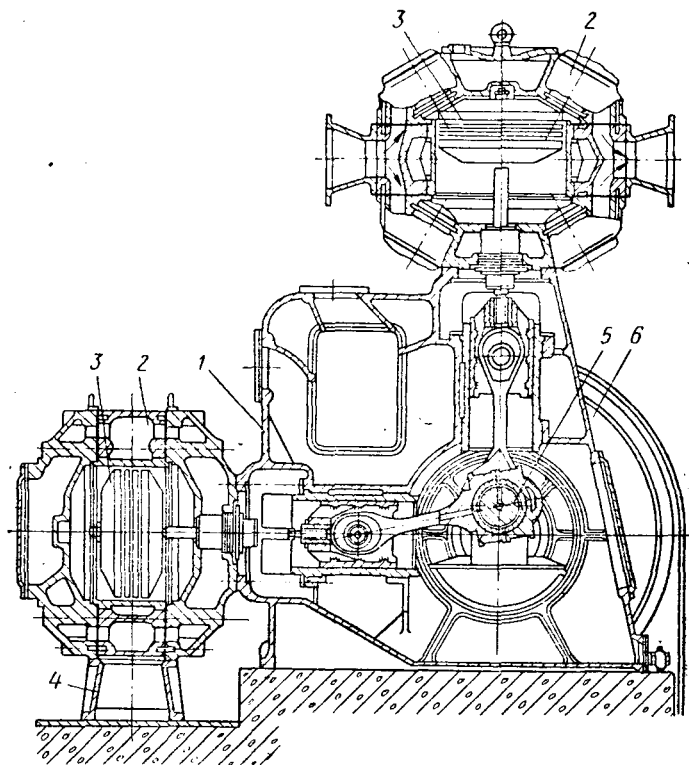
Угловой компрессор с прямоугольным расположением осей цилиндров:
